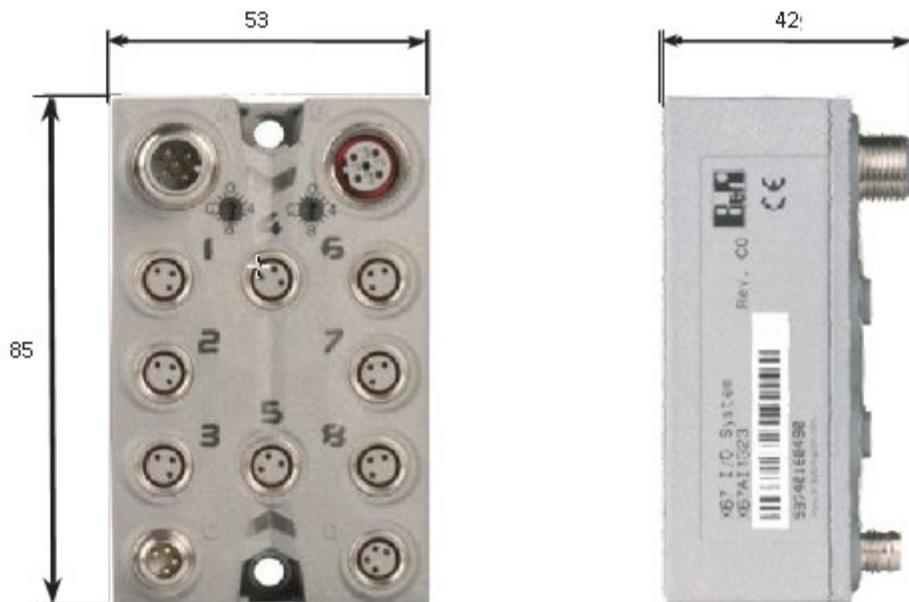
A. Dimensioni del blocco I/O di espansione (in millimetri).
